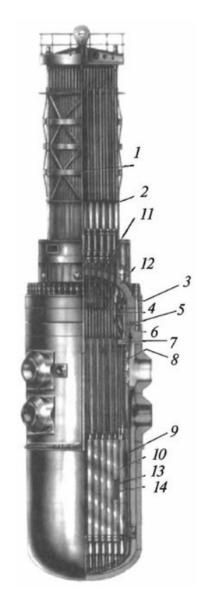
Общий вид реактора ВВЭР-1000 в сборе
